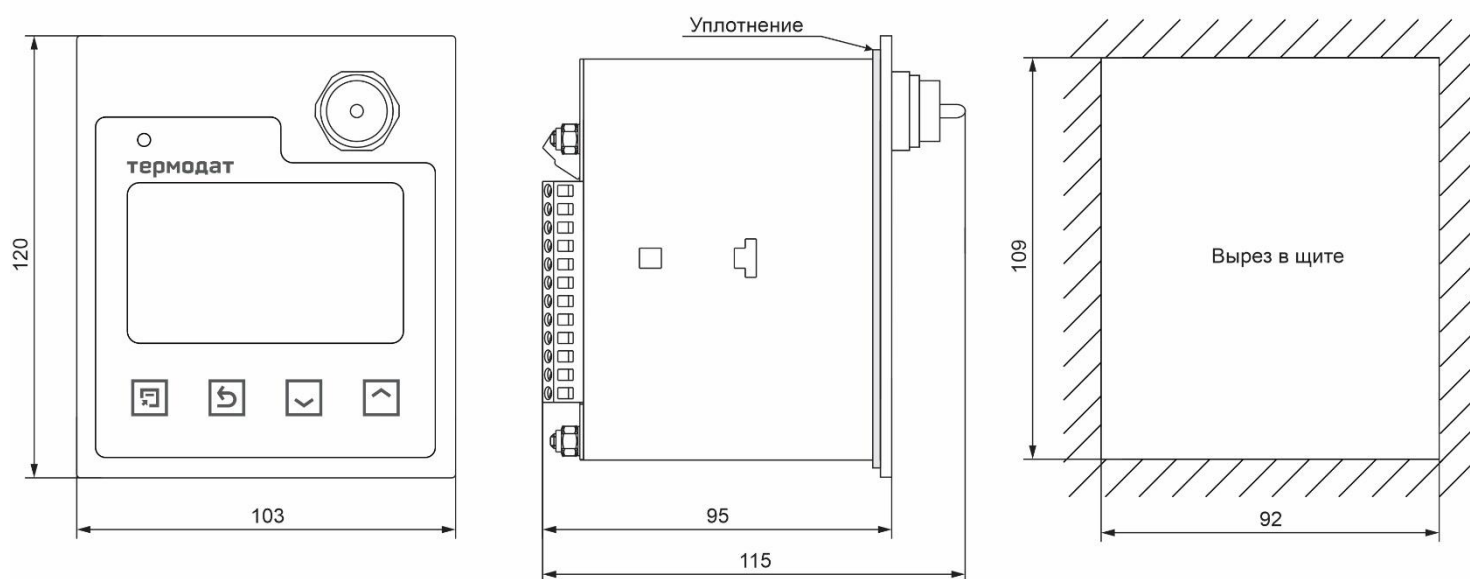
Габаритные размеры прибора Термодат-17Е6/...../F/IP67пп
